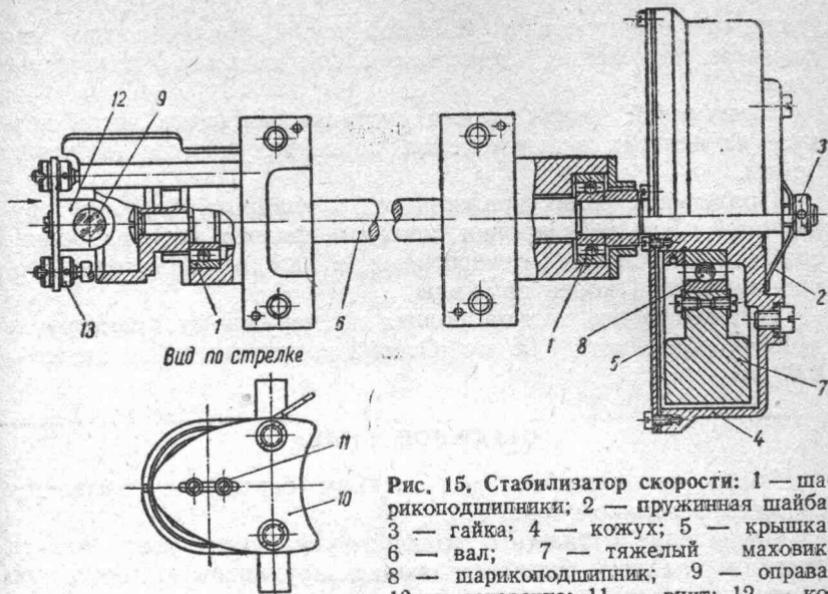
Стабилизатор скорости: 1 — шарикоподшипники; 2 — пружинная шайба; 3 — гайка; 4 — кожух; 5 — крышка; 6 — вал; 7 — тяжелый маховик; 8 — шарикоподшипник; 9 — оправа; 10 — основание; 11 — винт; 12 — колонка; 13 — гайка
